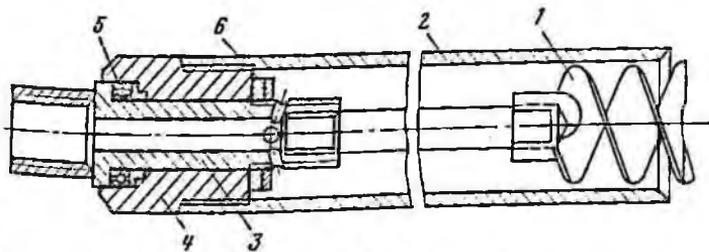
Шнекоколонковый снаряд конструкции Ф. А. Шамшева:
